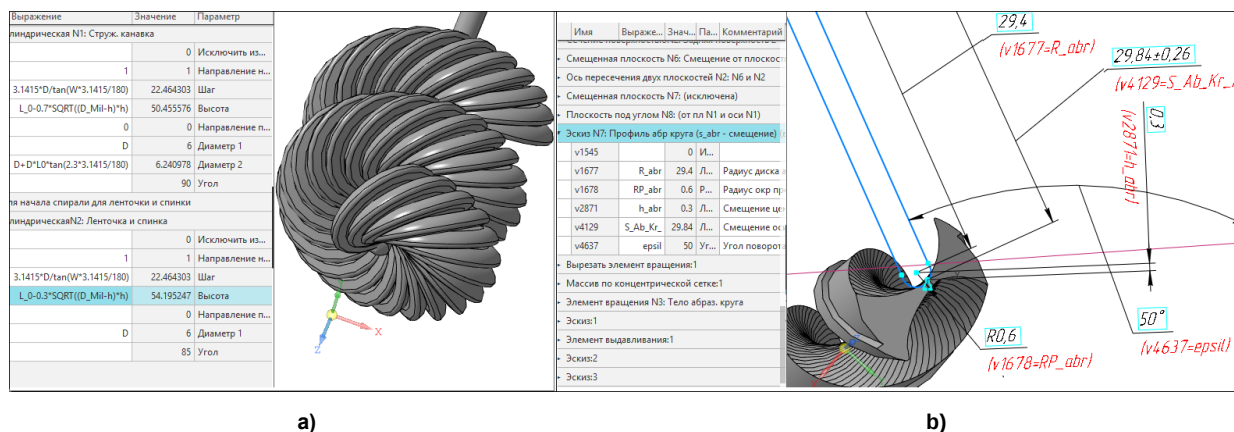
Семейство ИИП фрезы (а) и профиль шлифовального круга для подточки поперечной кромки (б)
